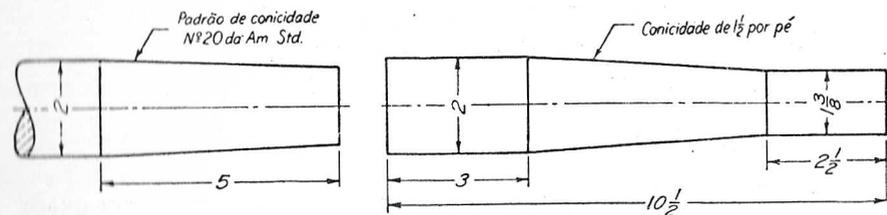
Modo de indicar a inclinação das partes cônicas
